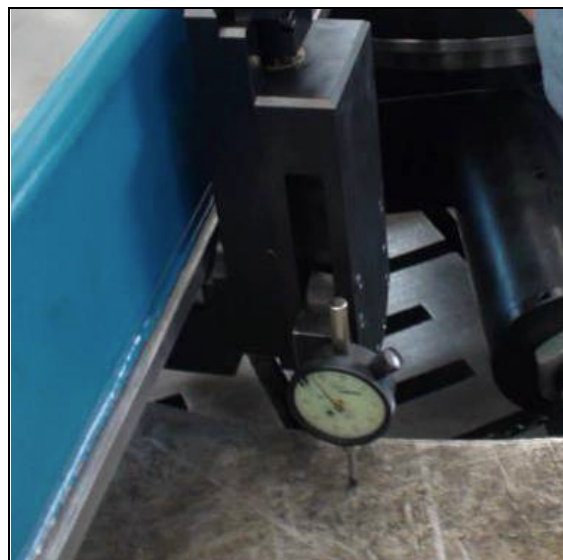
ПРИКРЕПЛЕННЫЙ ЦИФЕРБЛАТНЫЙ ИНДИКАТОР
